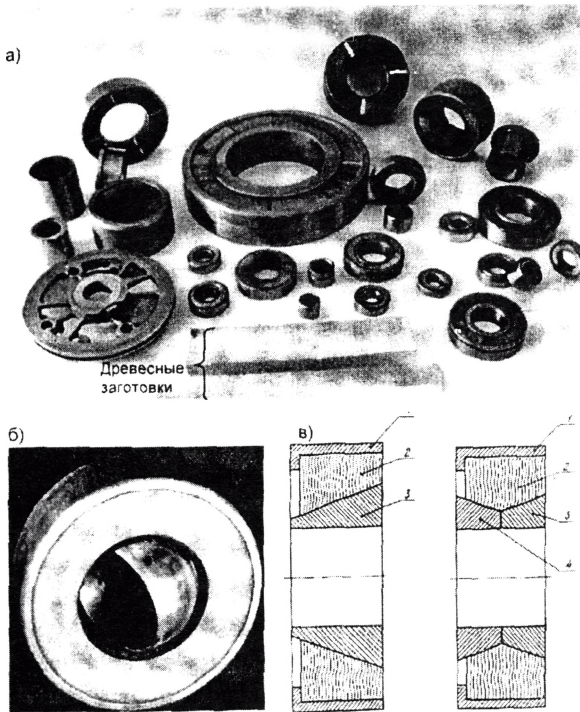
Различные конструкции подшипников скольжения на основе древесины объемного деформирования: а – ПСС с цилиндрическими поверхностями; б – со сферической поверхностью; в – с конической поверхностью
